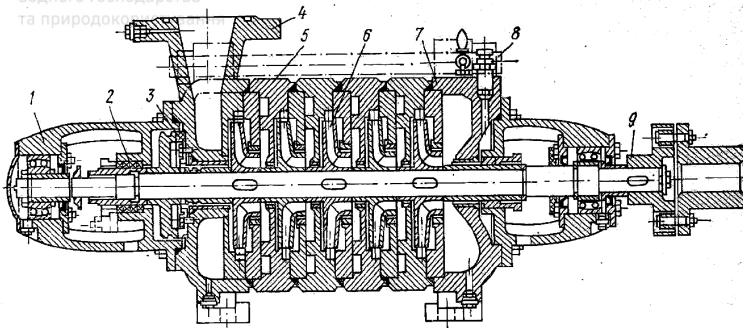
Поздовжній переріз багатоступінчастого насоса секційного типу: 1- корпус підшипника; 2- сальник; 3- гідроп'ята; 4- напірний патрубок; 5- секція; 6- робоче колесо; 7- кришка камери всмоктування; 8- стяжний болт; 9- пружна муфта.
